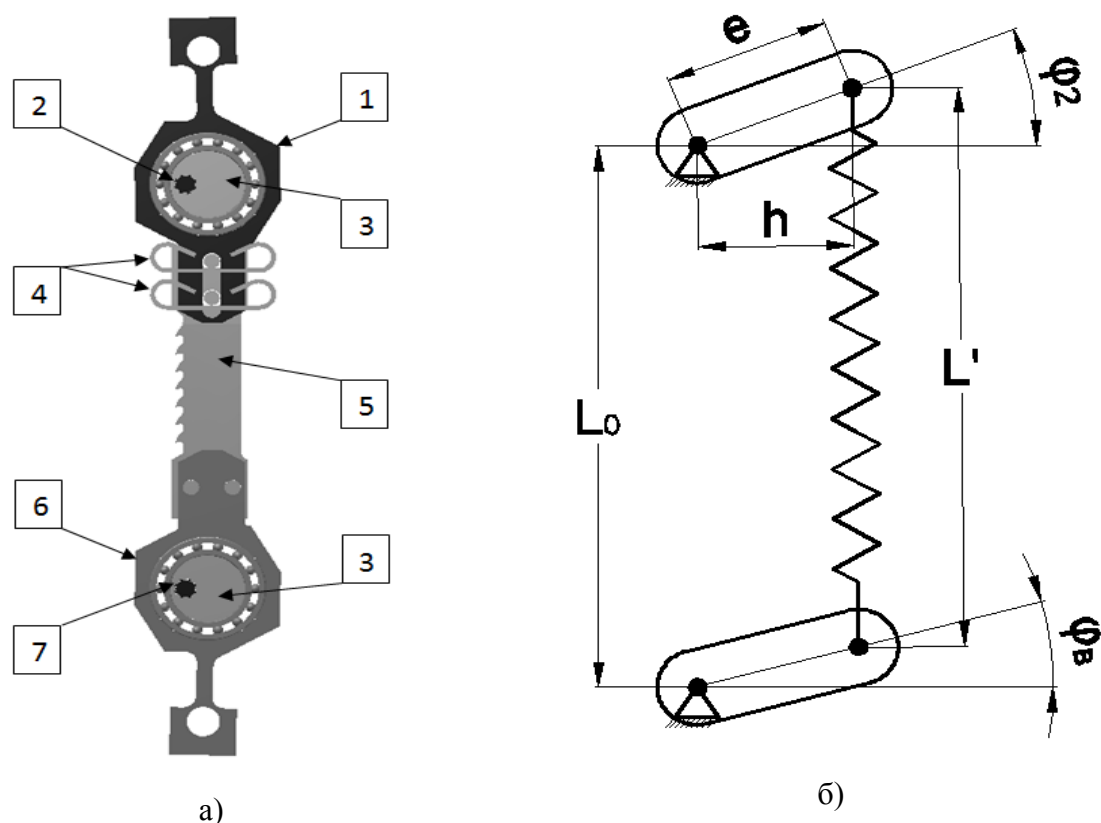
а) схема пильного модуля: 1 – верхняя корпусная деталь, 2 – верхний (ведомый) вал, 3 – эксцентрик, 4 – упругие элементы крепления пильного полотна, 5 – полосовое пильное полотно, 6 – нижняя корпусная деталь, 7 – нижний (ведущий) вал; б) расчётная схема пильного модуля.
